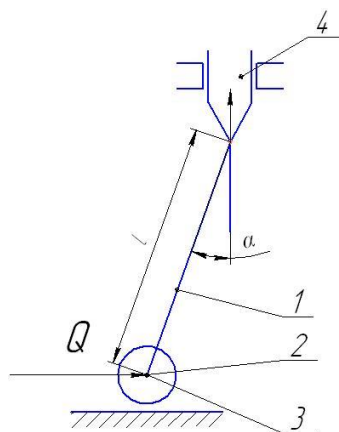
Схема однорычажного рычажно-шарнирного механизма: 1 - рычаг; 2 - шарнир (ось рычага); 3 - ролик, 4 - плунжер
